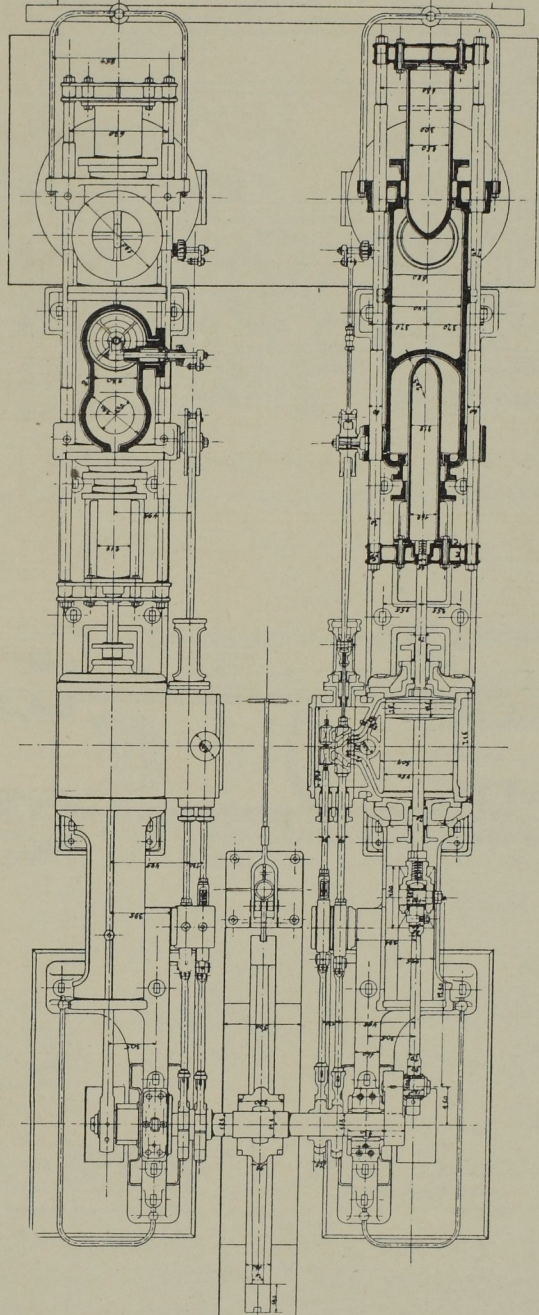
Grundriss der Maschine und Längsschnitt. Masst. 1 : 75.
